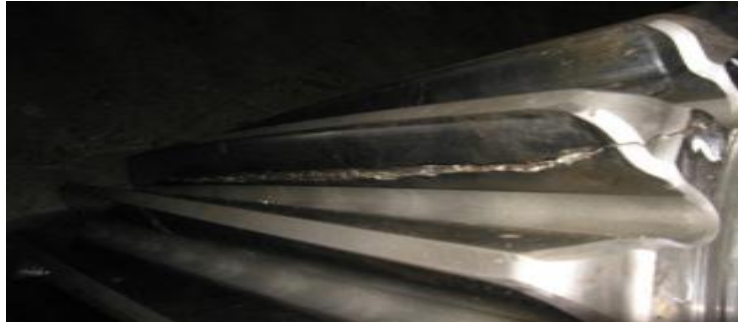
Fissuration ou crack d'un engrenage [7]
